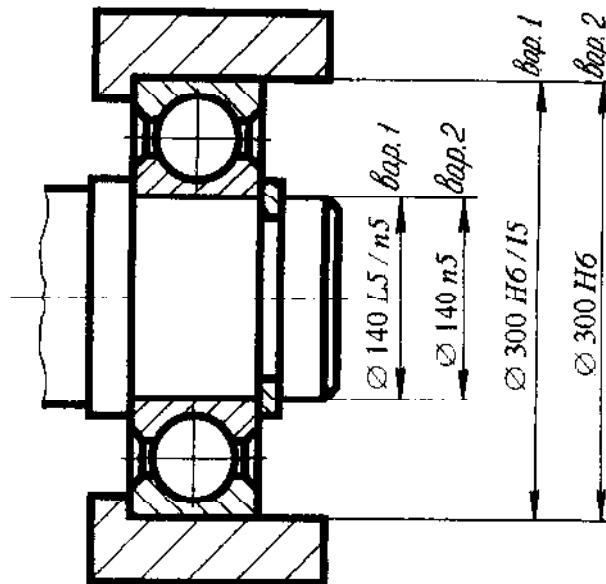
Ескіз робочого креслення з'єднання підшипника з валом і отвором корпуса
